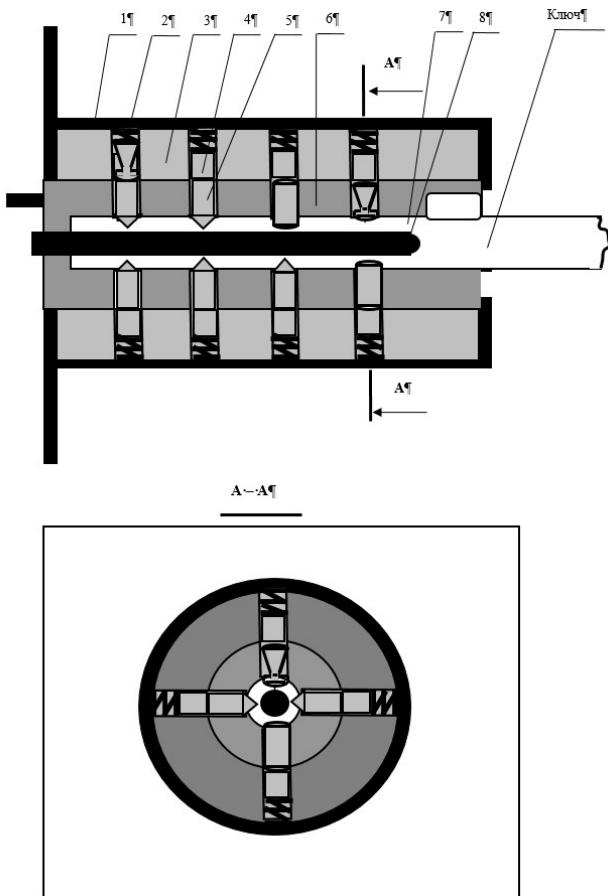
Штифтовий механізм секрету ЦШЗП ТYTAN ZX фірми «Gerda»: 1 – захисна накладка; 2 – пружини; 3 – корпус; 4 – ЗШ; 5 – КШ; 6 – циліндр; 7 – ключ; 8 – стрижень циліндра
